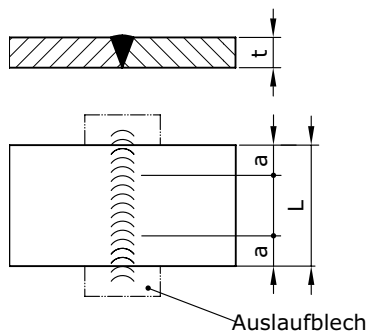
WS) Definition der Schweissnahtdicken und -längen am Flachstab
